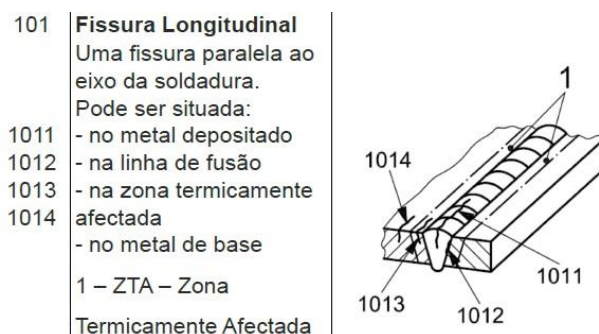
Ilustração da fissuração longitudinal pela norma ISO 6520
